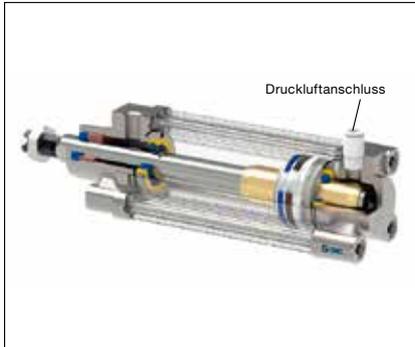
Pneumatikzylinder mit Druckluftanschluss
